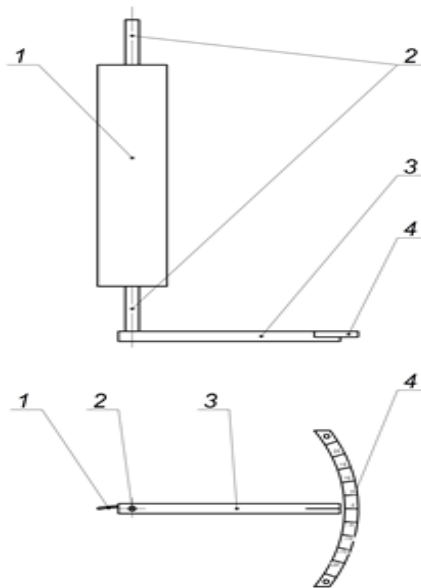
Схема конструктивна механізму керування направляючих лопаток: 1 – направляюча лопатка; 2 – консоль; 3 – важіль; 4 – сектор керування
